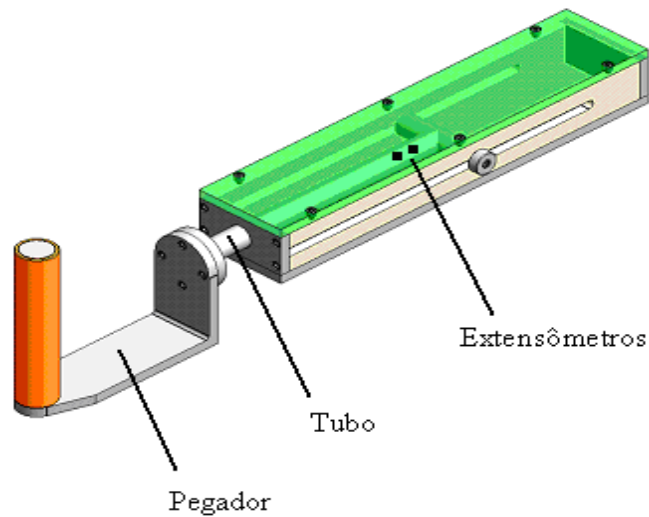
Desenho esquemático com detalhes do Dispositivo de Medição de Esforços.
